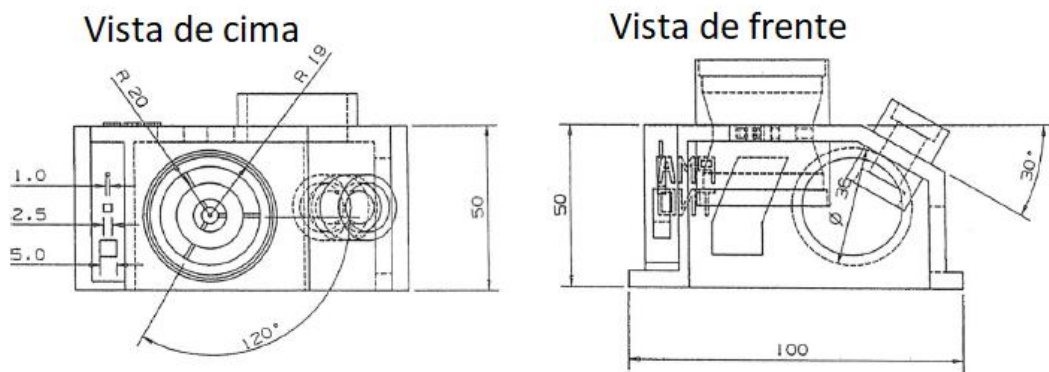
peça de benchmarking proposta por Kruth. Adaptado de (Rebaioli & Fassi, 2017).
